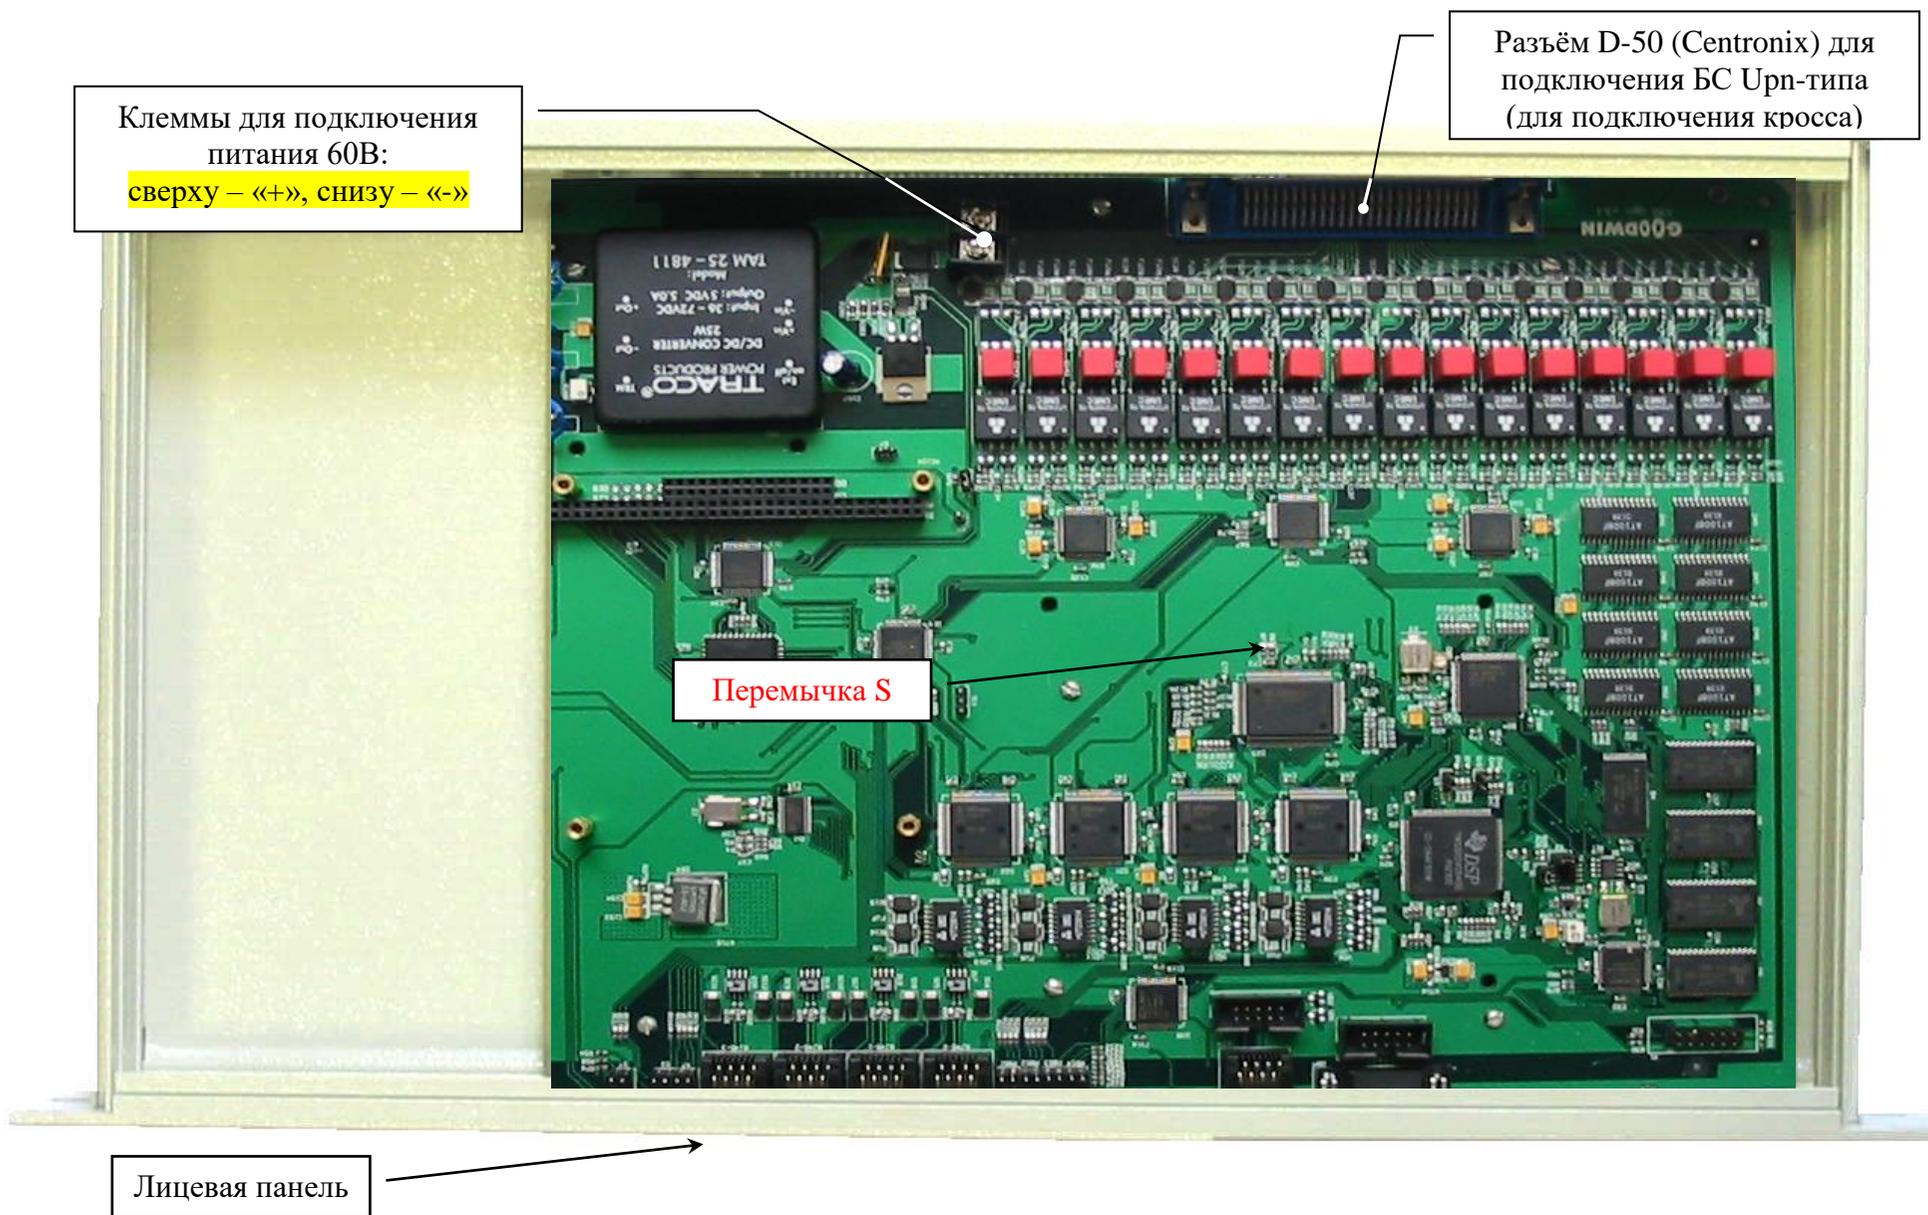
а. Конструкция МБС-Урп с питанием - 60/-48 В (вид сверху, без крышки) [Обновить фото](#)
